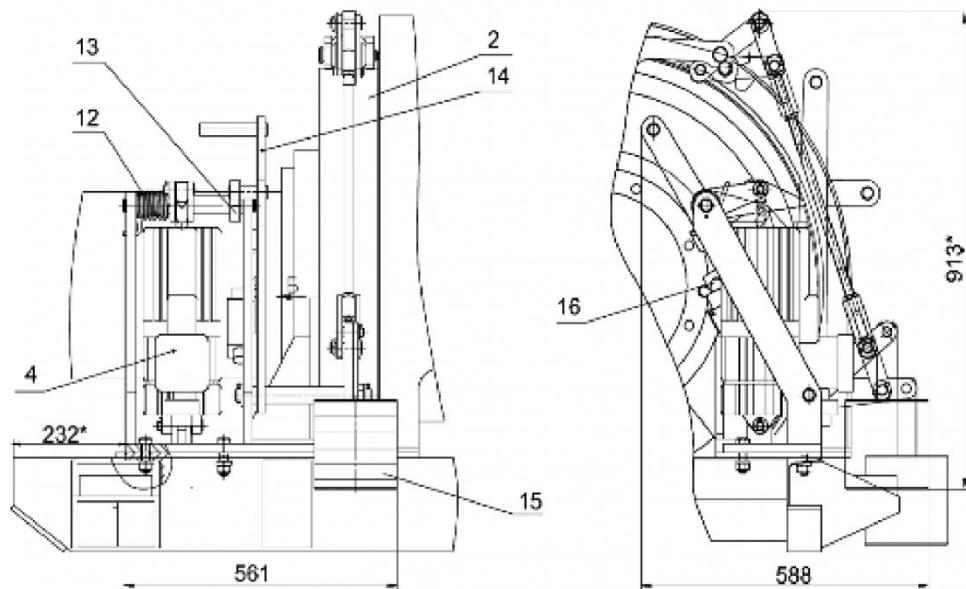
Рабочий (а) и предохранительный (б) тормоза подъемной установки
